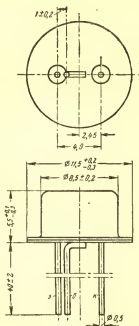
Габаритный чертеж транзисторов П20—П21А.
